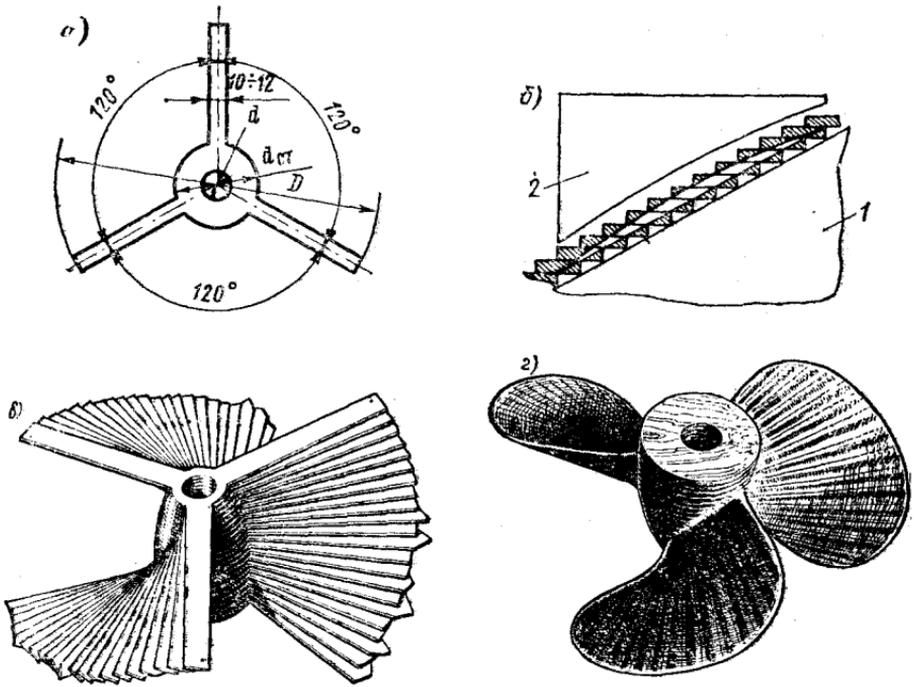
Изготовление модели гребного винта из фанеры: а — «звездочка»; б — обработка лопасти по шаблону; в — заготовка из стеклянных «звездочек»; г — готовая модель винта. 1 — шаговый угольник; 2 — контршаблон.
